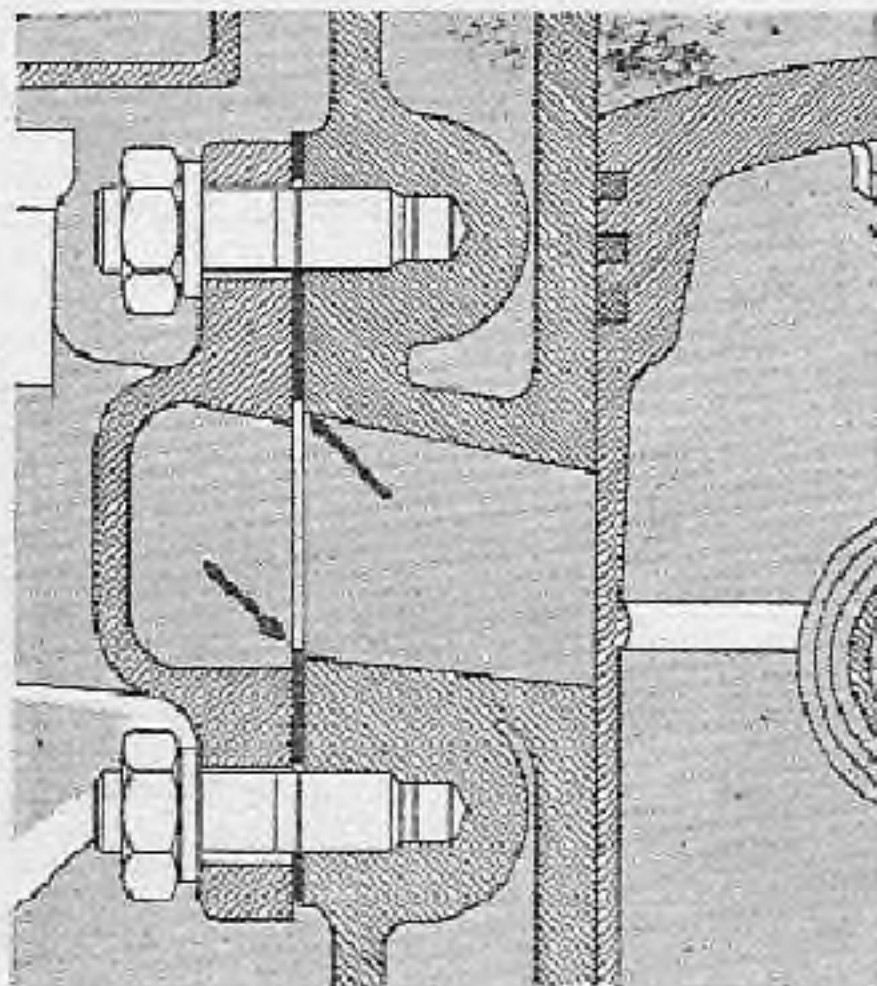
Montaje incorrecto del múltiple de admisión.
